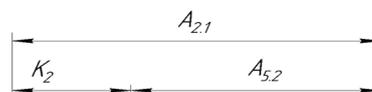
Размерная цепь, содержащая конструкторский размер  $K_2$
